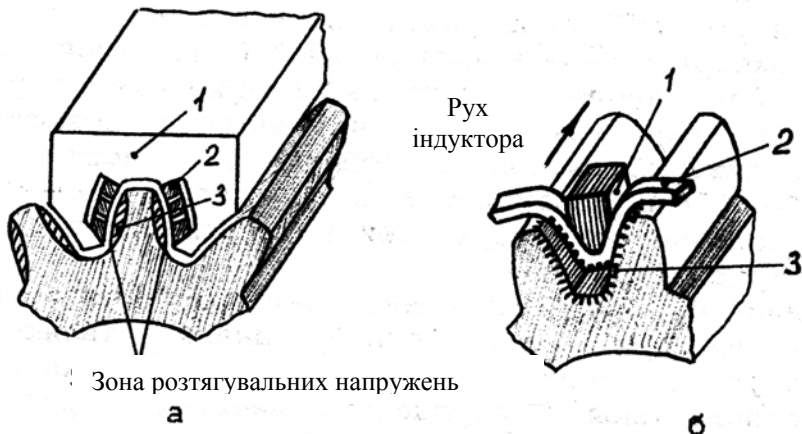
Схеми гартування зубчастих коліс: а - «зуб за зубом»; б) - «по западині» (1 - магнітопровід; 2 - індуктор; 3 - нагрітий шар)
